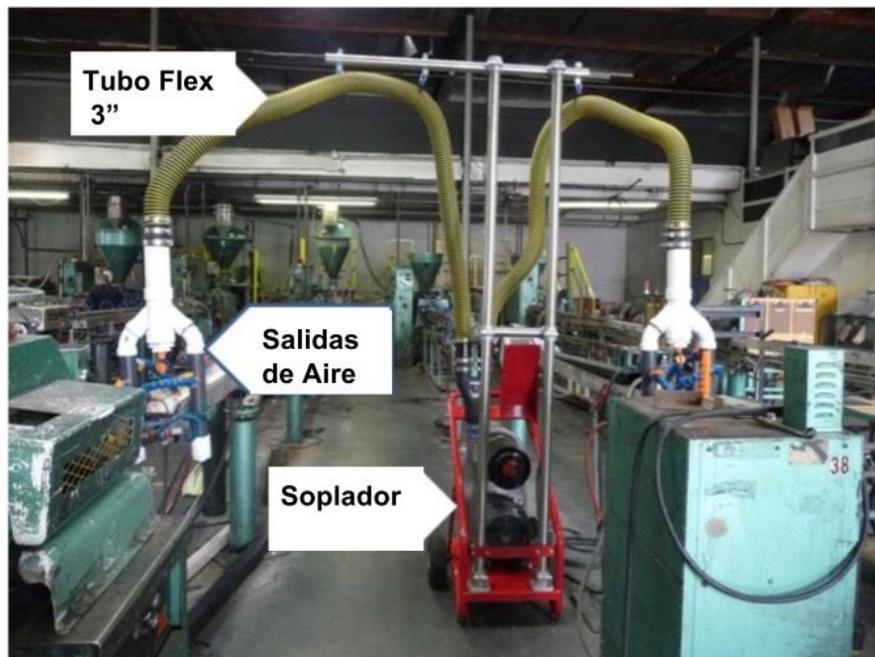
SISTEMA DE SOPLADOR INSTALADO EN EL SITIO DE PRUEBAS
